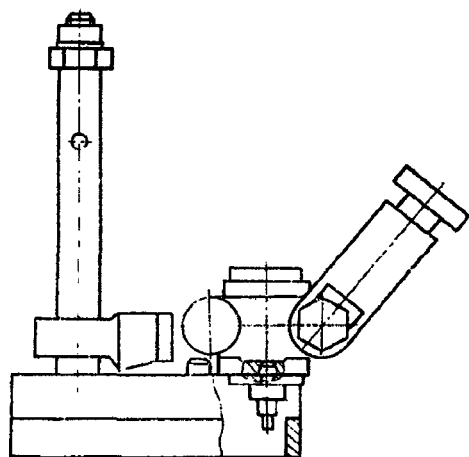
Установка топливного насоса низкого давления в приспособление И801.20.000 для разборки-сборки
